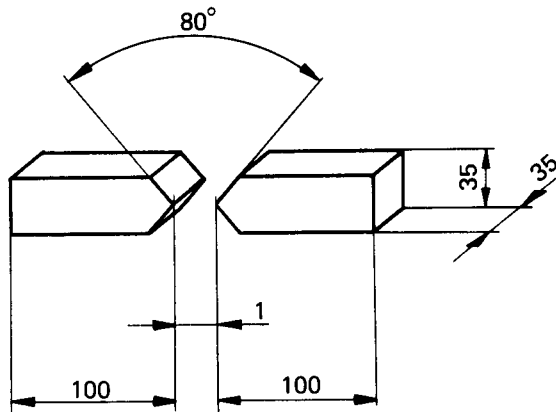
Préparation de l'assemblage pour soudobrasage (fonte) FIGURE 5 – Dimensions de l'éprouvette préparée (fonte)
